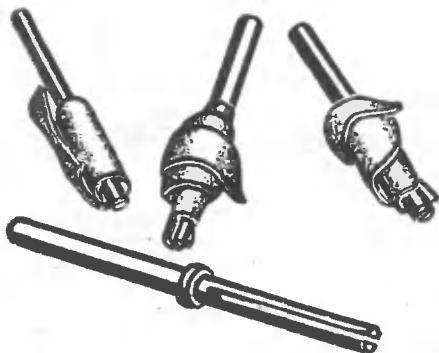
Шлифовальные головки из шкурки и оправка к ним.
